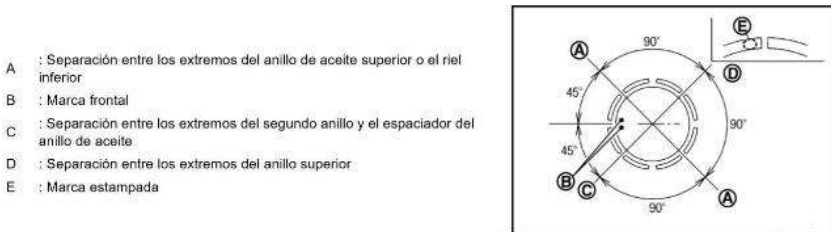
Pautas para el montaje de anillos en pistón motor. Nissan motor company.
